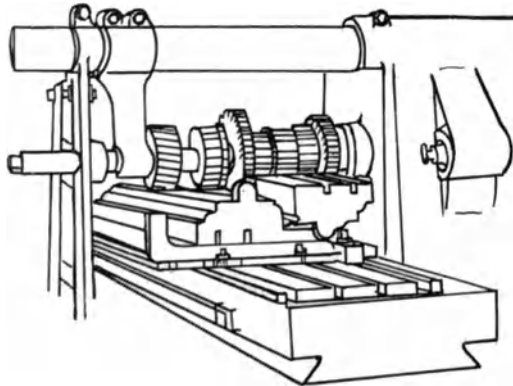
Das Fräsen mit 2 verschiedenen Frälersätzen.
